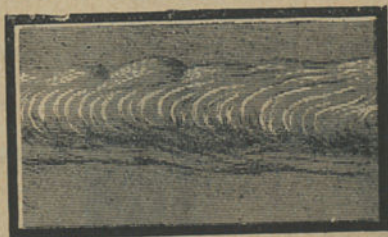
Soldadura de chapa de alumínio de 4 m/m.
